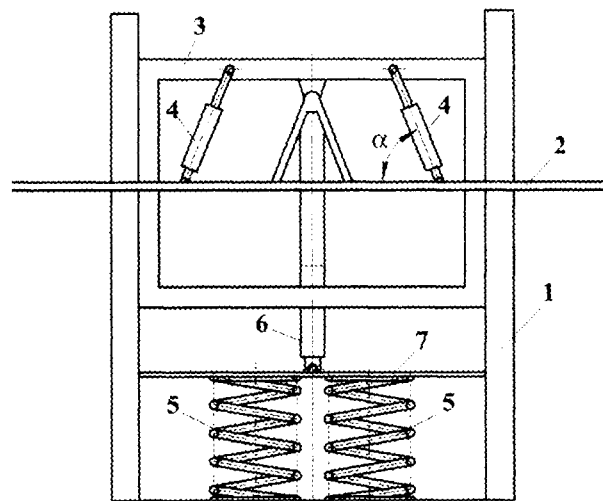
Схема к расчету вертикальных пружин: 1 – вертикальные направляющие рамы опрыскивателя; 2 – несущая конструкция штанги; 3 – подвижная рамка; 4 – амортизаторы; 5 – пара пружин; 6 – гидроцилиндр регулировки высоты установки штанги
